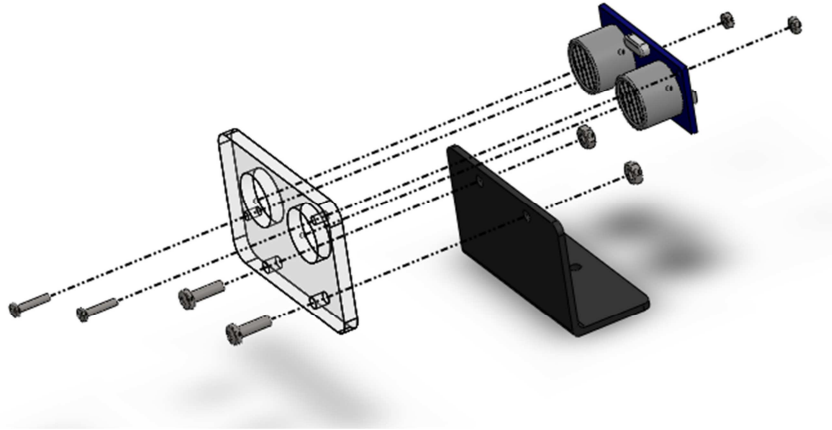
Vista explosionada del montaje de los sensores traseros.
